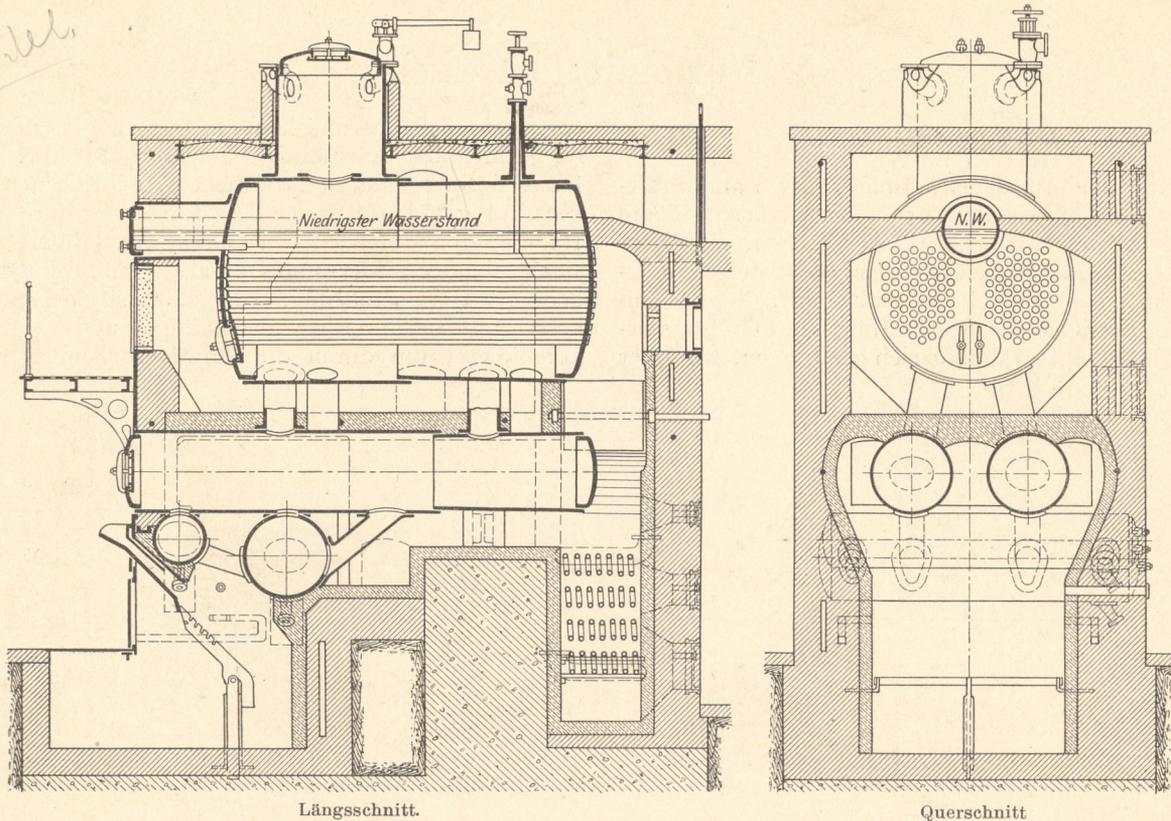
Rauchrohrkessel, kombiniert mit Längs- und Quersiedern.
